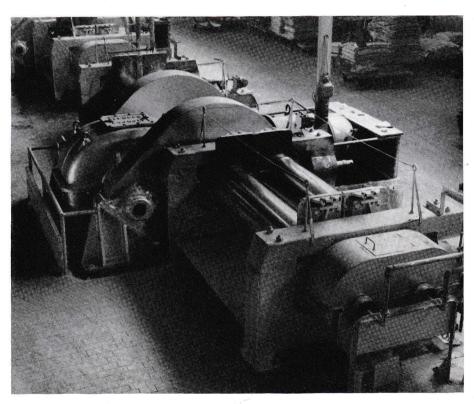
Laminador tándem de goma — 660/564×2135 mm Rodamientos: rodamientos de rodillos a rótula 23072 K/C3
